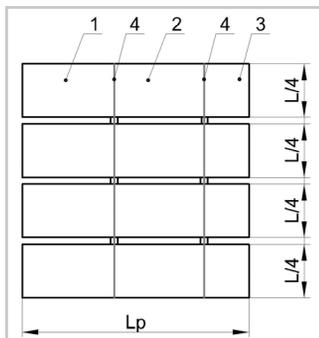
Схема одновременной сварки разверток дополнительных цаг удлиненных обечайек: 1, 2 и 3 – листы разверток цаг; 4 – соединительная планка; 5 – сварной шов; L – длина обечайки; L_p – длина развертки цаги
